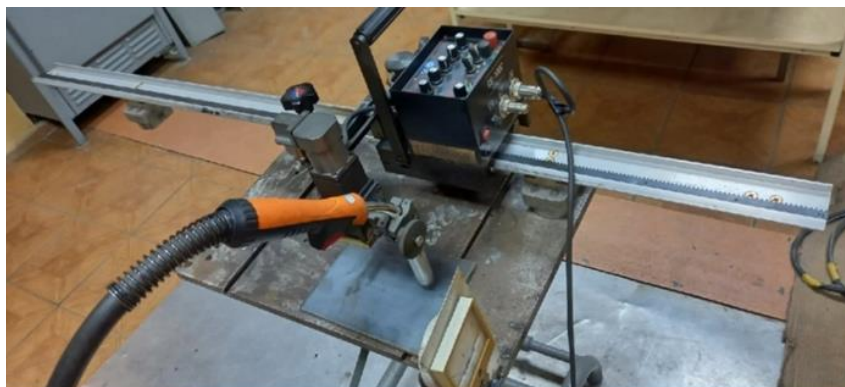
Общий вид используемой каретки с установленной сварочной горелкой
